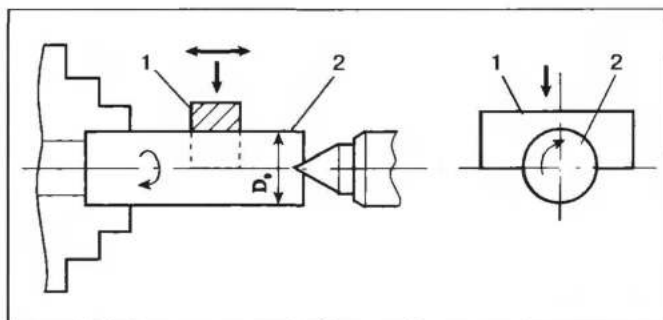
Схема притирки поверхности постели на деформированной крышке коренного подшипника:
